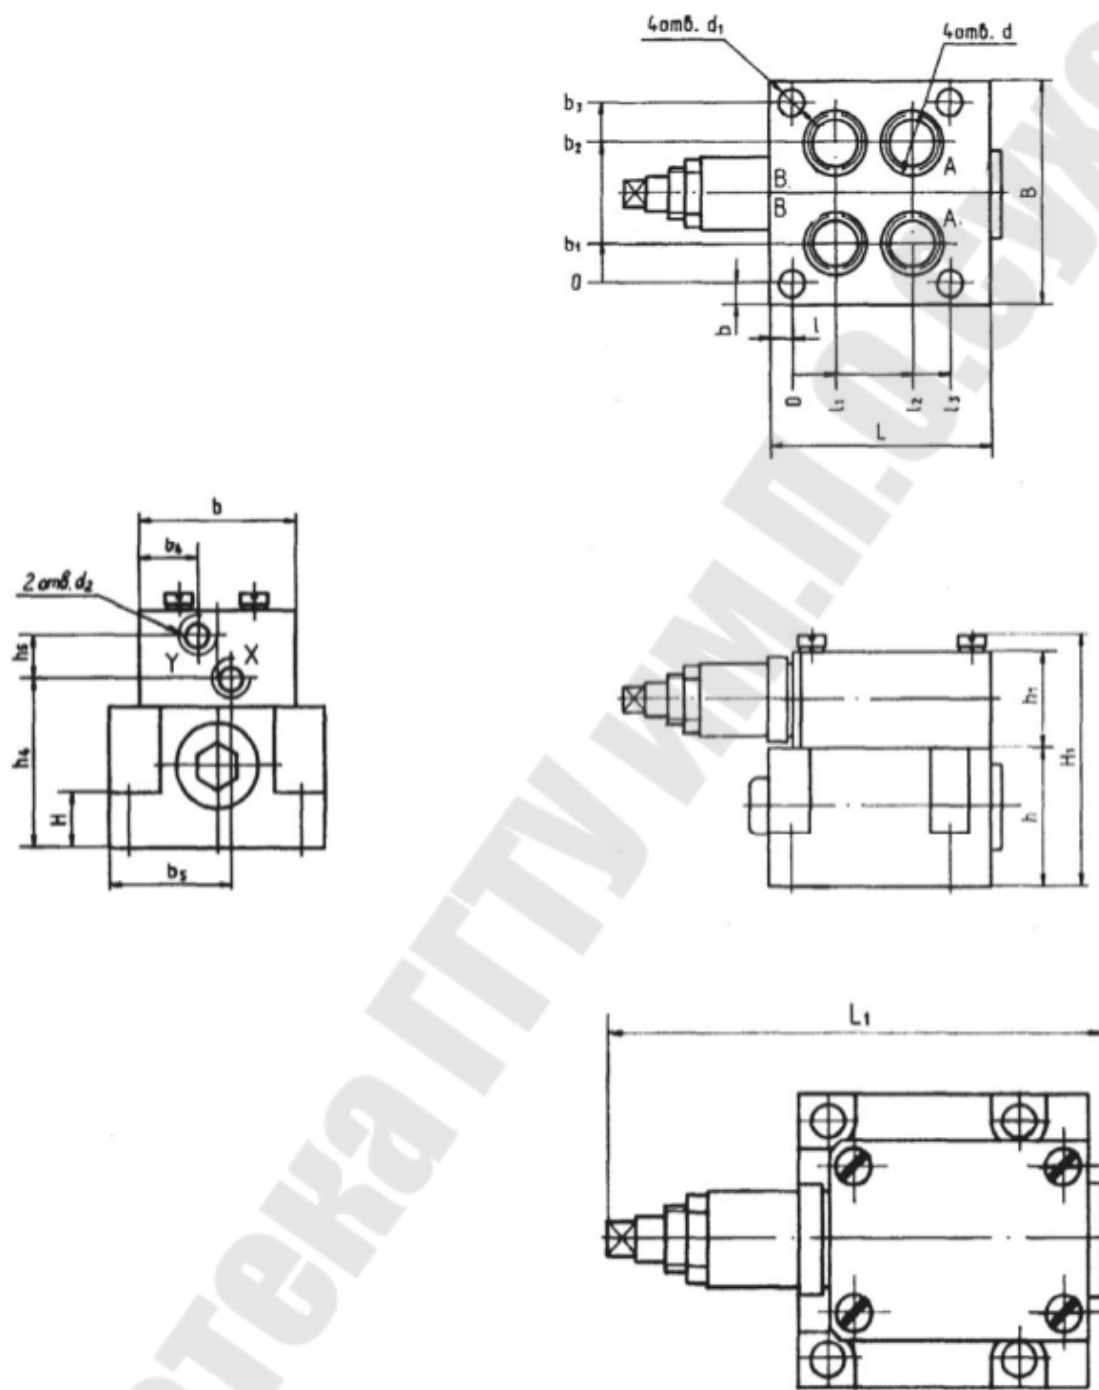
Общий вид блока присоединительного клапана редукционного БВП-6КР
